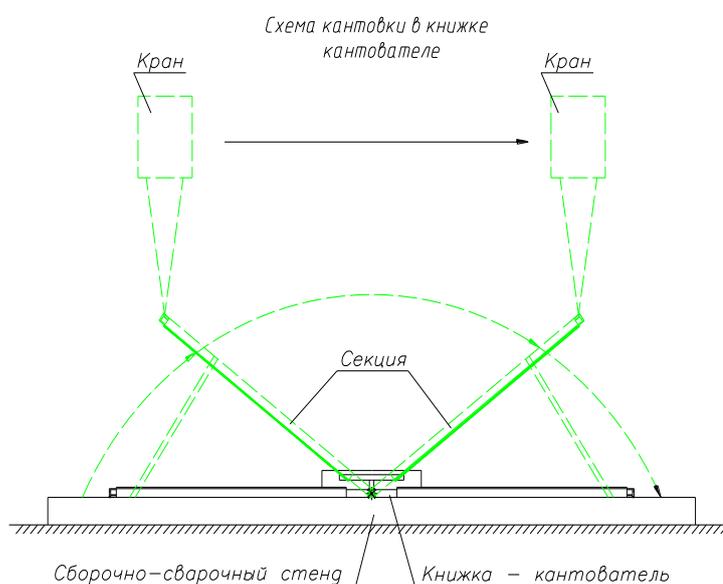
Сборочно-сварочный стенд, оснащенный книжкой-кантователем
